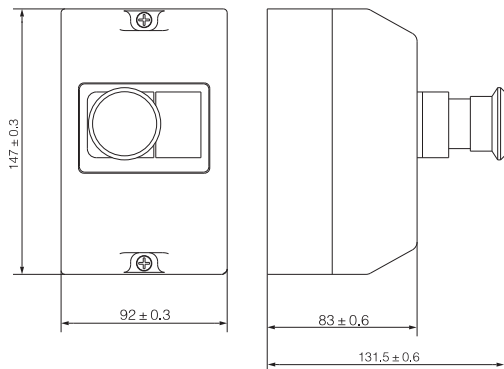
Габаритные и установочные размеры оболочки защитной
